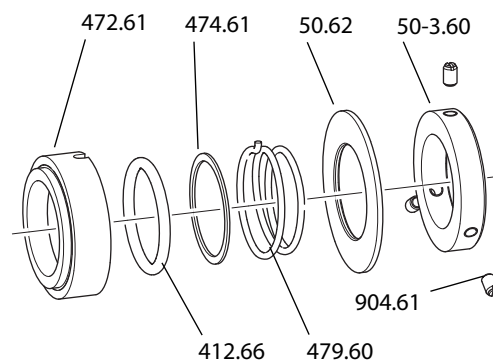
Caso d'applicazione D, montaggio della tenuta meccanica sul lato motore (I)
